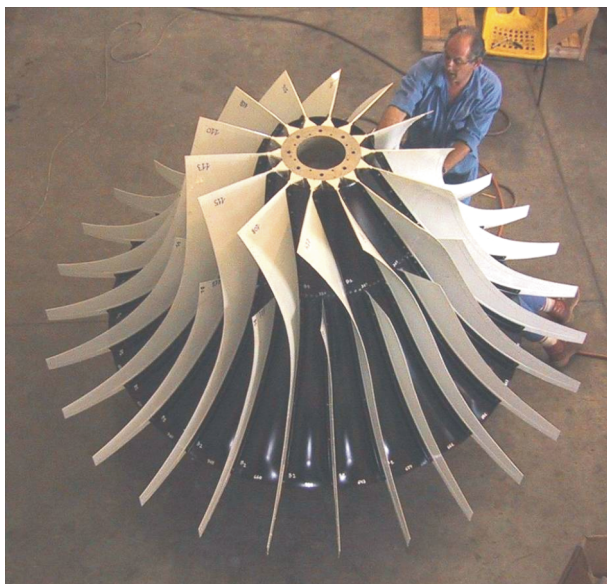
Внешний вид колеса центробежного турбокомпрессора
